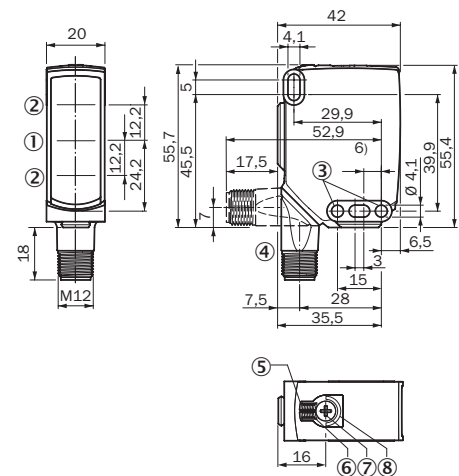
Масштабный чертёж 1, штекер WTS16
